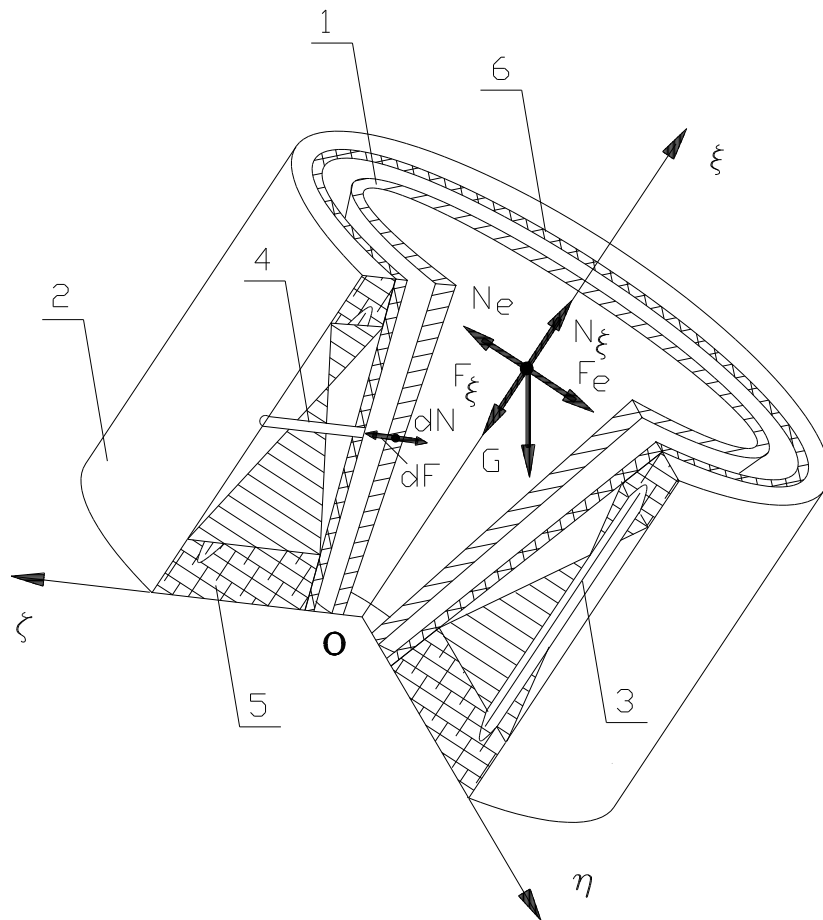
Газомагнітний підвіс конічного ротору. 1 - конічний гістерезисний ротор; 2 - статор з конічною розточкою; 3 - обмотка статора; 4 - живильники-дроселі подачі стислого газу; 5 - наповнювач з немагнітного матеріалу; 6 - шар з немагнітного матеріалу на робочій поверхні ротору.
